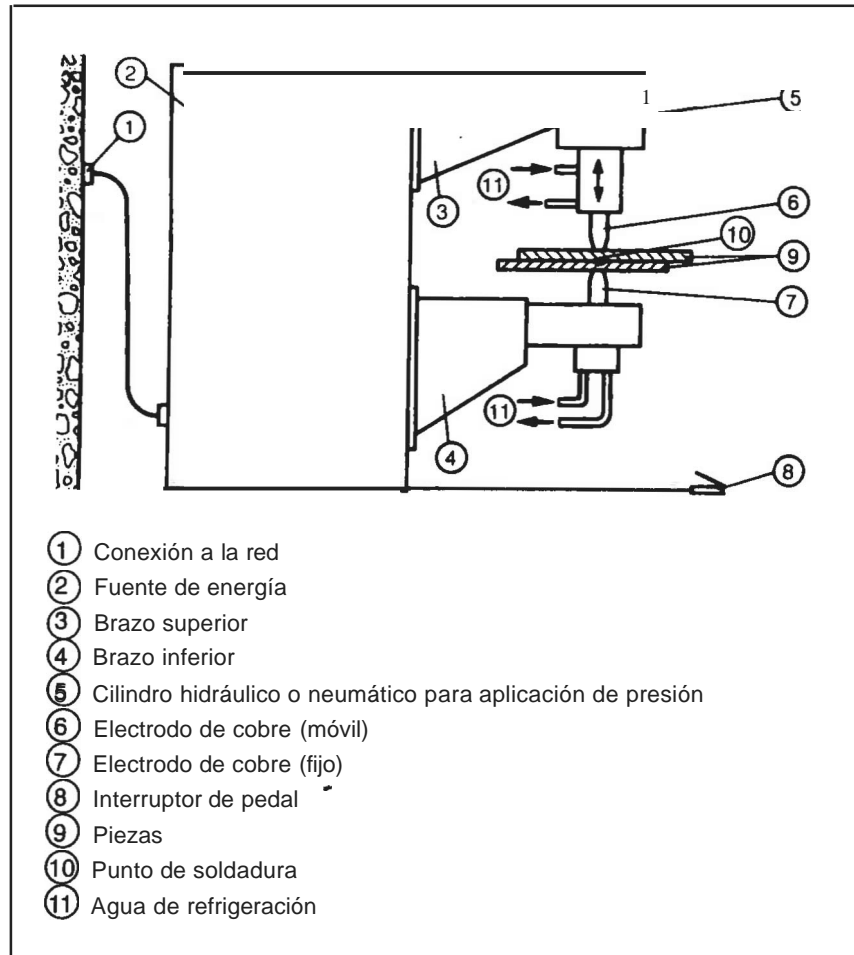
EQUIPO DE SOLDEO POR PUNTOS
